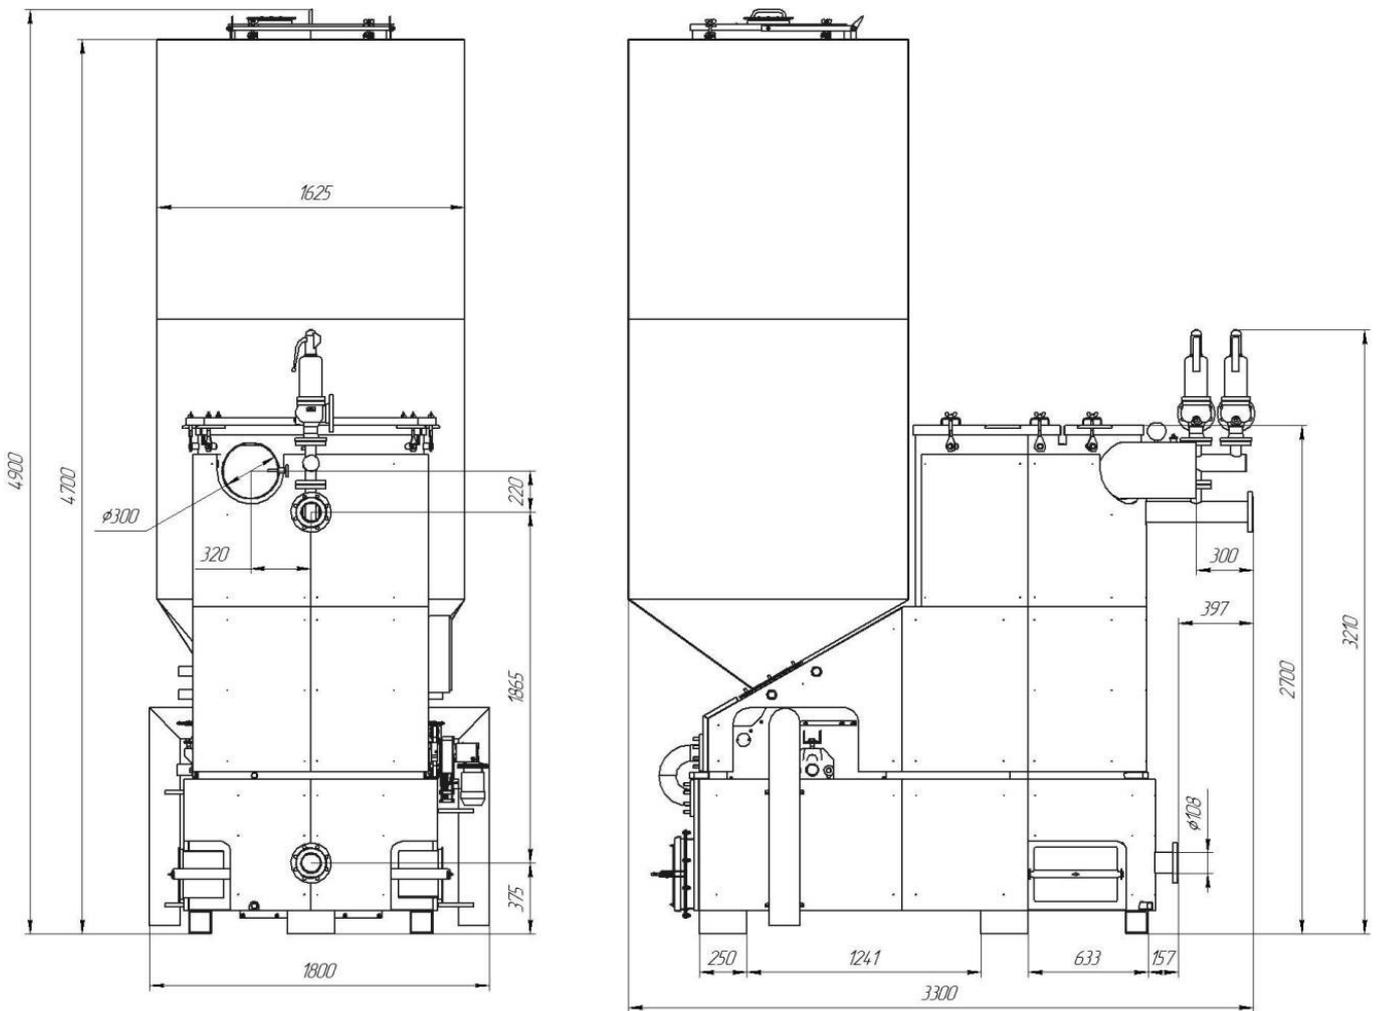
Эскизы котла Прометей-Автомат-600М с габаритными размерами
